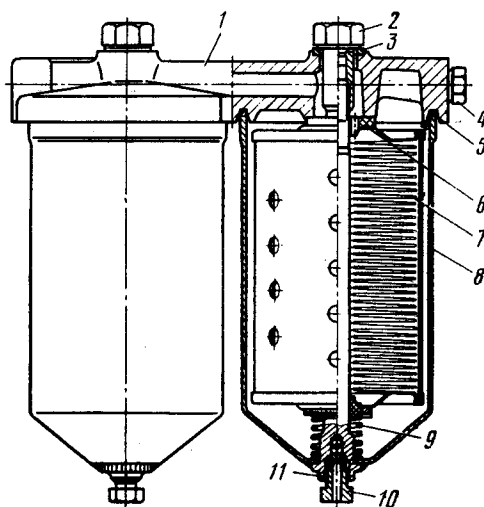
Фильтр тонкой очистки топлива: 1 — корпус; 2 — болт; 3 — уплотнительная шайба; 4, 10 — пробки; 5, 6 — прокладки; 7 — фильтрующий элемент; 8 — колпак; 9 — пружина фильтрующего элемента; 11 — стержень
